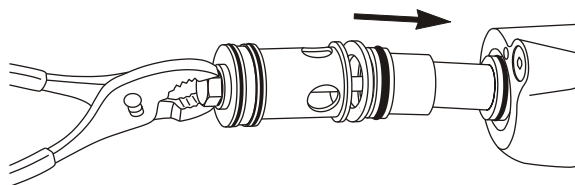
Выталкивание с противоположного конца для извлечения золотника клапана.
